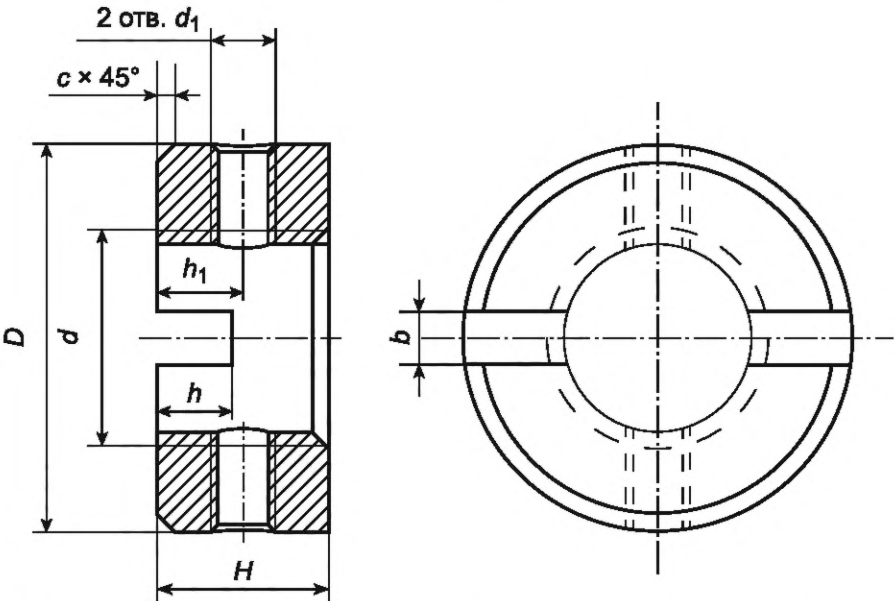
Конструкция круглых гаек со шлицем и отверстиями для стопора
